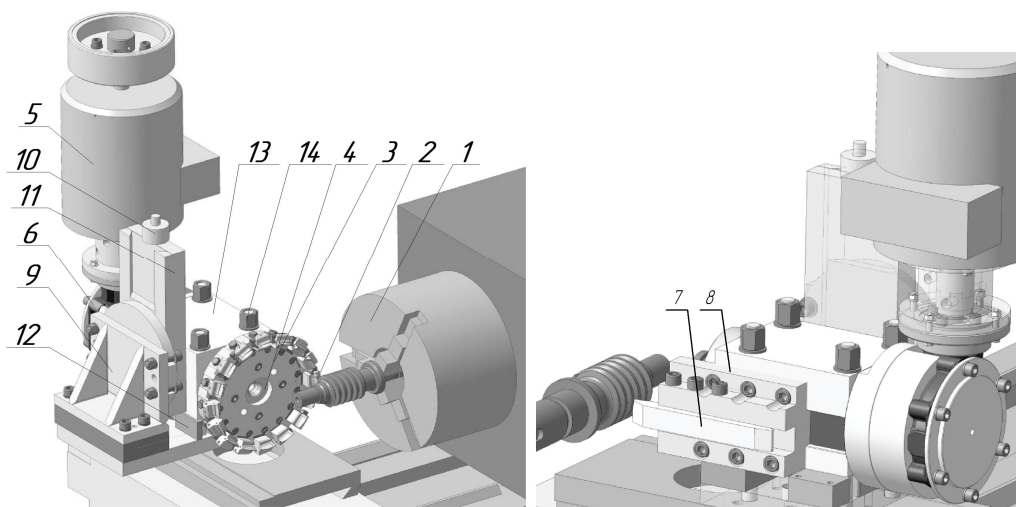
Токарный станок с ЧПУ 16A20Ф3, модернизированный для нарезания витков червяков торцевой резцовой головкой
